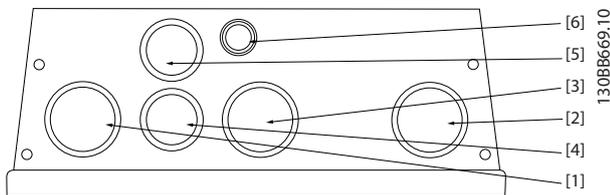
B1 - Kabeleinführungsöffnungen mit Gewinde IP55
